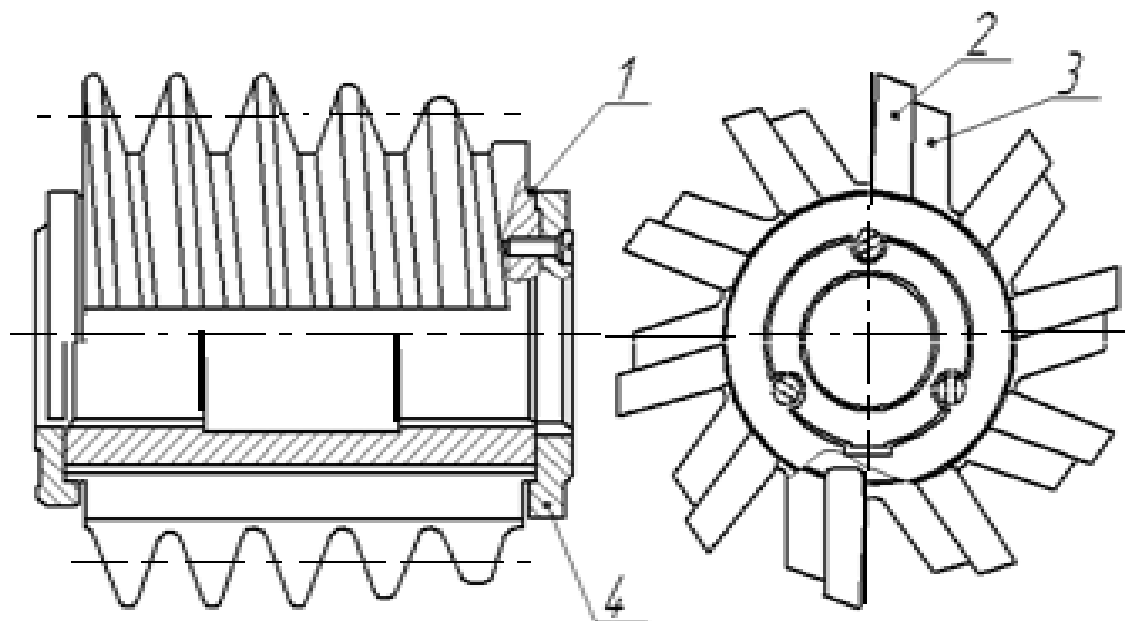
Червячные фрезы $m=5-16\text{мм}$, с припаянными контактно-реактивной пайкой, зубчатыми рейками:
